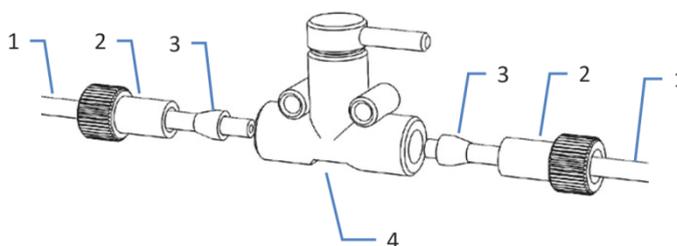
Installation d'une vanne d'arrêt sur la conduite de solvant
